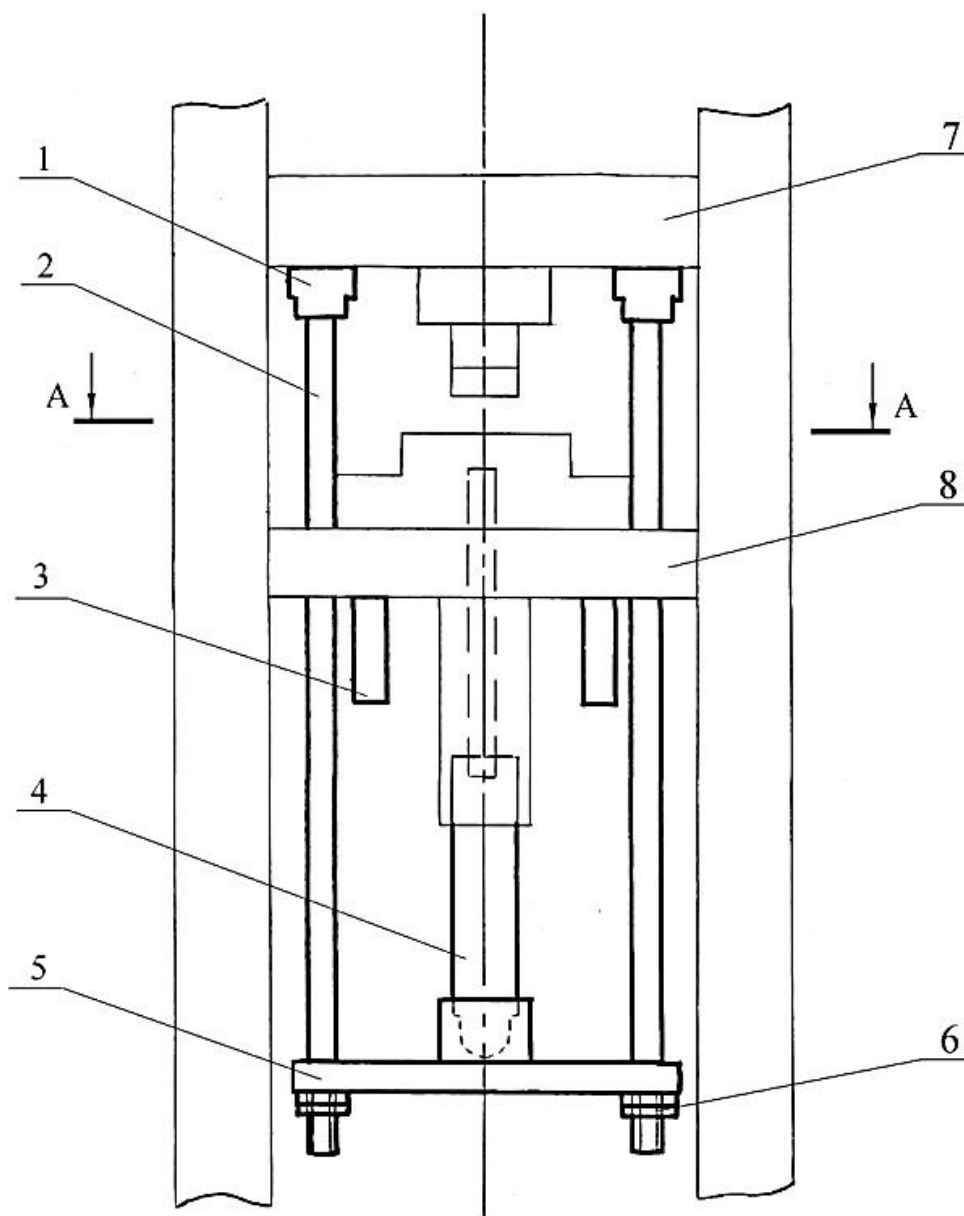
Схема расположения механизма выталкивателя (вид сбоку):
